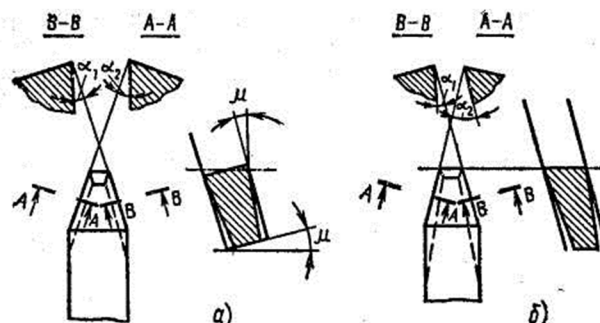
Установка резьбового резца при нарезании трапецидальной резьбы
